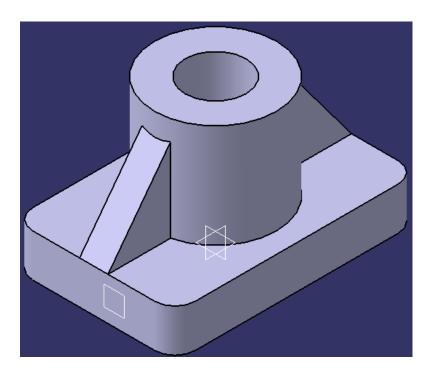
Трехмерная модель заготовки, изометрический вид
